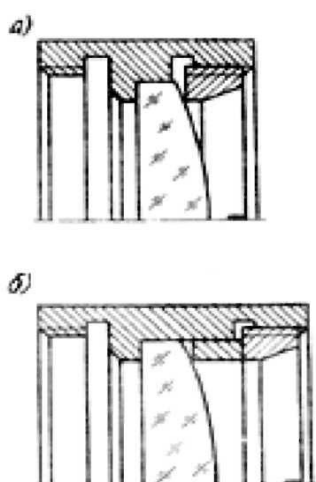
Крепление оптической детали резьбовым кольцом
